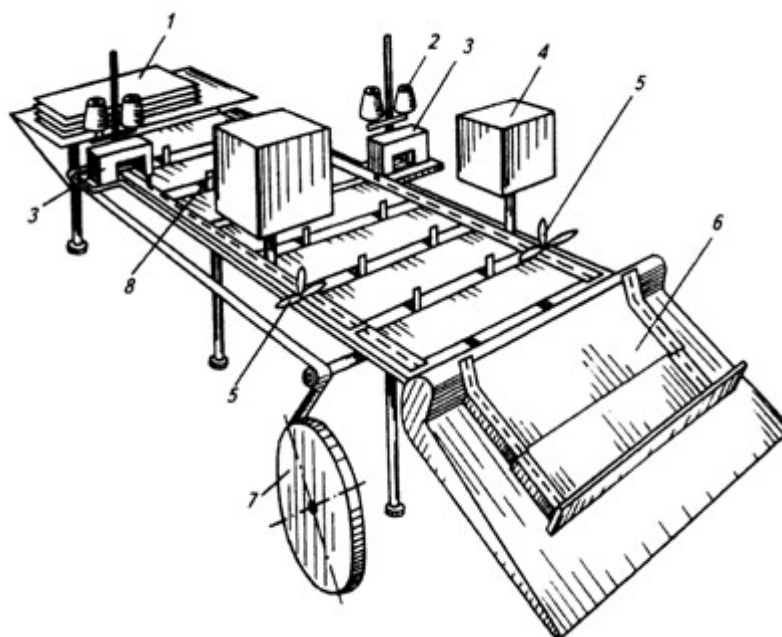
Схема швейного агрегата: 1 – штабель трубок; 2 – нить; 3 – швейные головки; 4 – устройство для герметизации прошитых швов; 5 – ножи; 6 – приемный стол; 7 – бобина; 8 – цепной транспортер
